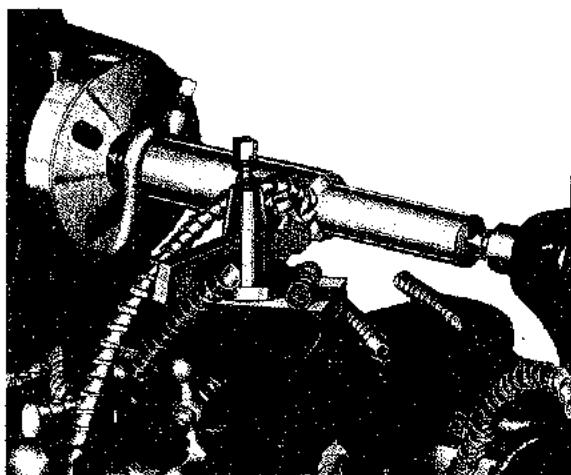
El torneado en un torno produce una pieza cilíndrica (South Bend Lathe Works).
